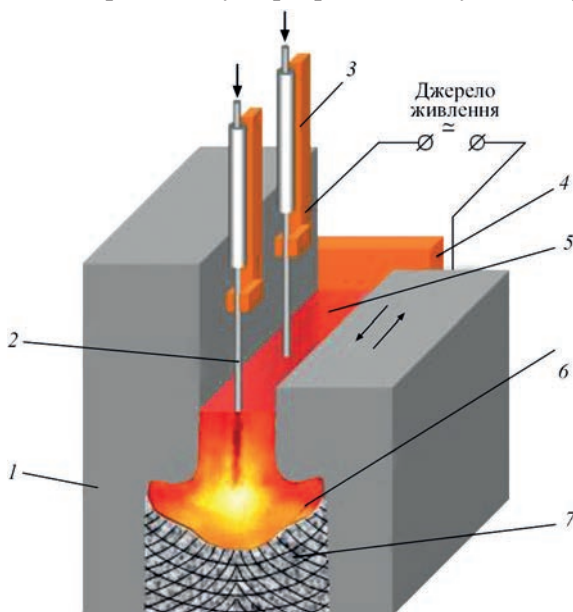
Схема ESW електродними дротами: 1 – зварювана кромка; 2 – електродний дріт; 3 – струмопідвод; 4 – водоохолоджуваний повзун; 5 – шлакова ванна; 6 – металева ванна; 7 – зварний шов
